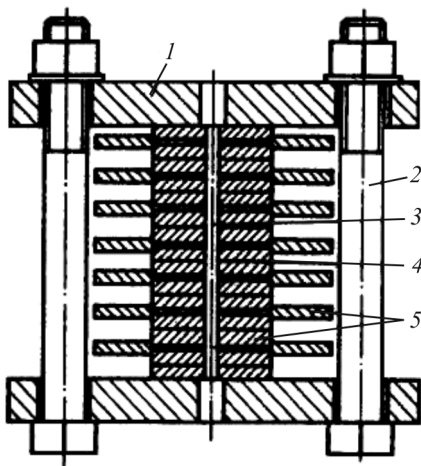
Приспособление для пакетной диффузионной сварки с использованием термонатяга: 1 – фланец; 2 – стяжной болт; 3 – центрирующее отверстие; 4 – компенсирующие прокладки; 5 – свариваемые детали
